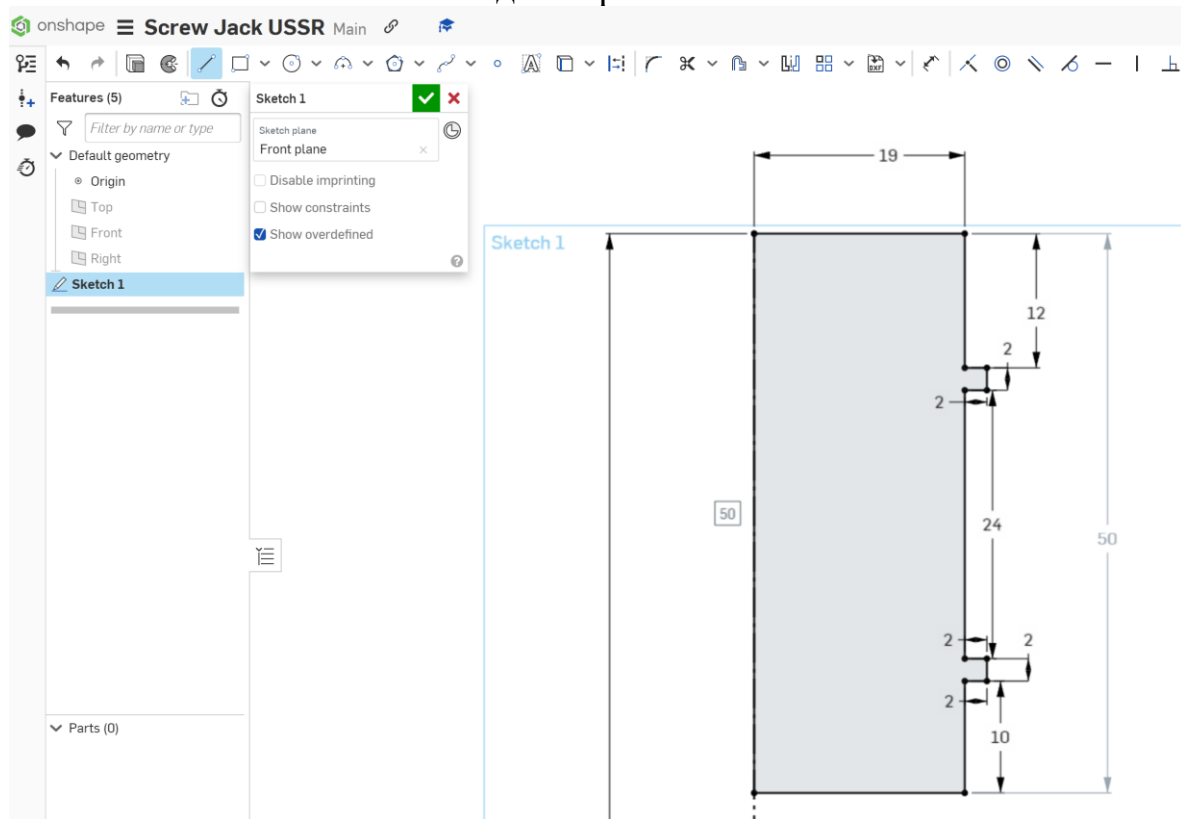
Готовий замкнутий ескіз для операції обертання
